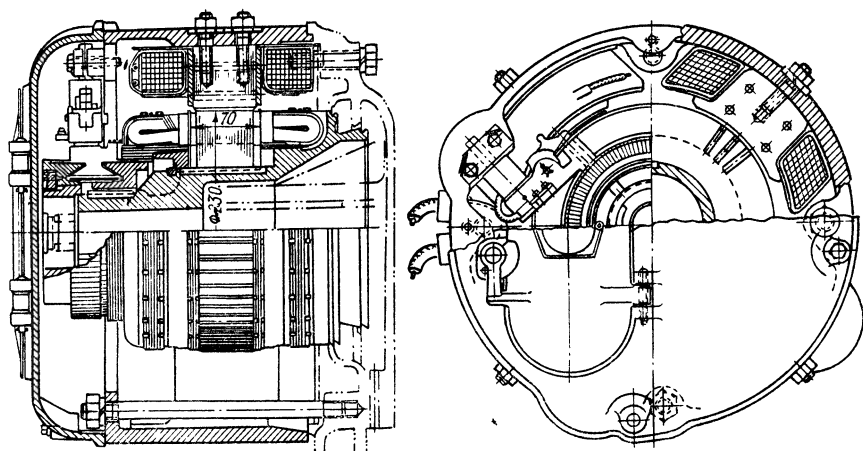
Двигатель компрессора Э-300 для трамвая
